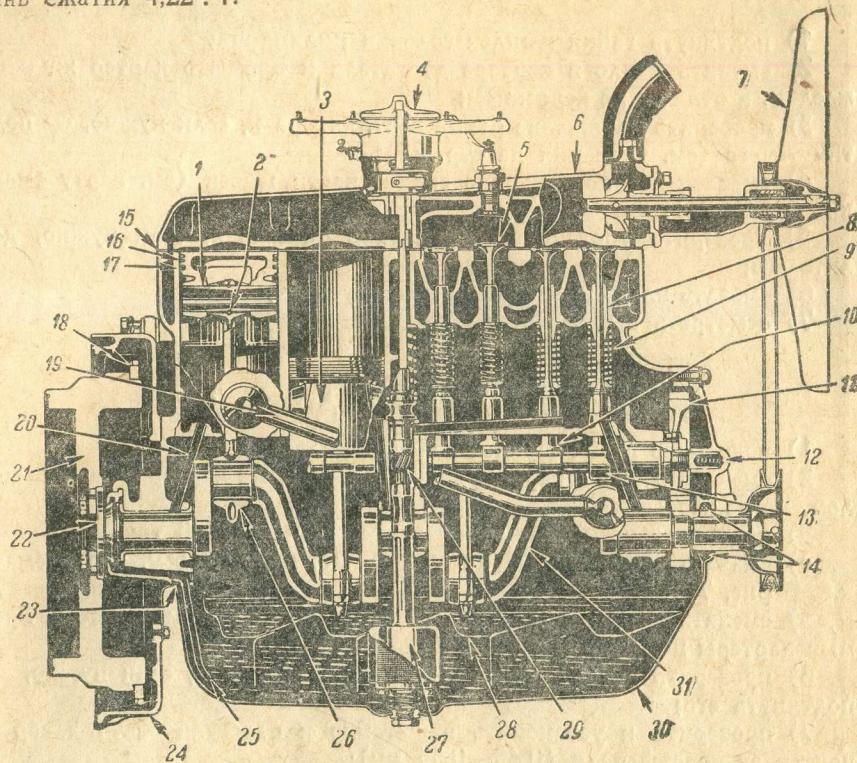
Продольный разрез двигателя ГАЗ-А:
